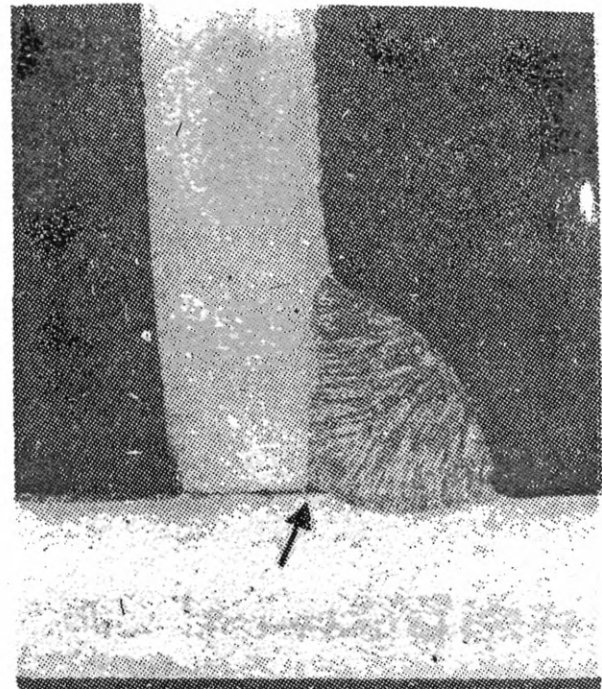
Непровар вершины угла при автоматической дуговой сварке стали 12Х18Н10Т проволокой ЭП-765 в аргоне, травление в реактиве № 5 (см. табл. 1),  $3\times$
